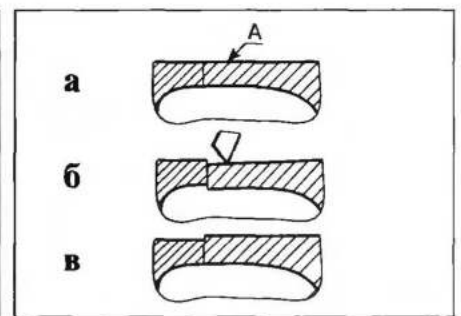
Типичный случай "проявления" трещины после обработки детали: А — обрабатываемая поверхность; а — фрагмент детали перед обработкой; б — отжим стенки детали инструментом; в — образование ступени после работы
